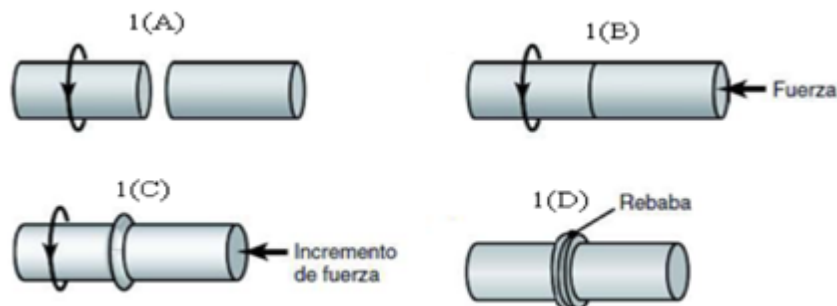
Proceso básico de la soldadura por fricción.
